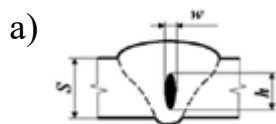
Схематическое изображение сварного шва и определение размеров дефектов при разбраковка,
